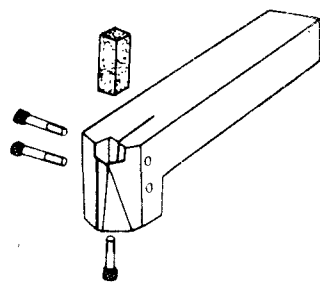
Инструмент с механическим креплением твердосплавной пластинки
